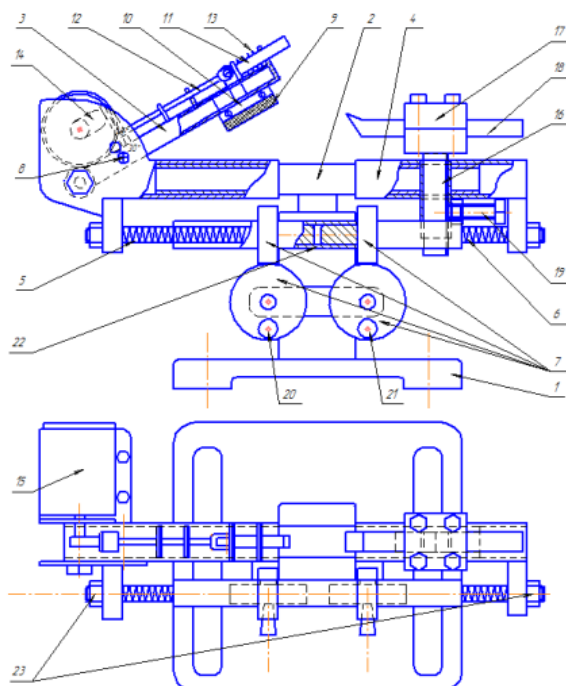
Схема приспособления для шлифования фасок и тарелок клапанов двигателей
